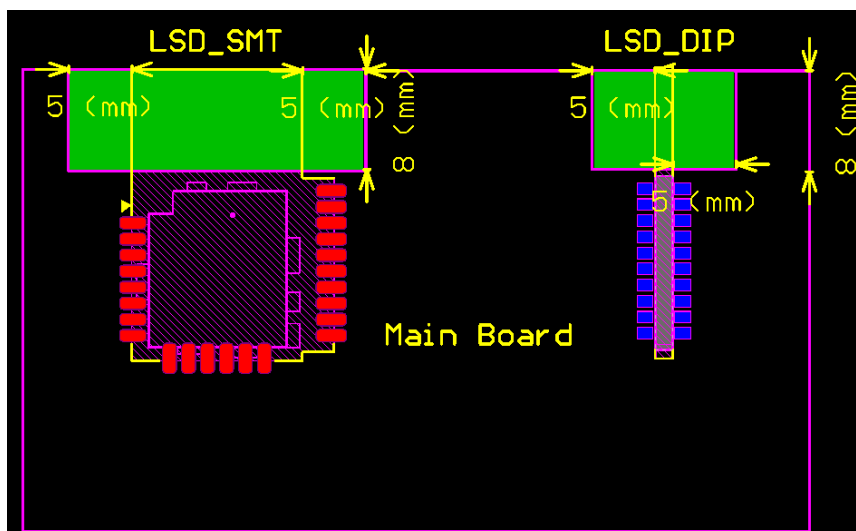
PCB 天线沿板边放置且下方均不敷铜
